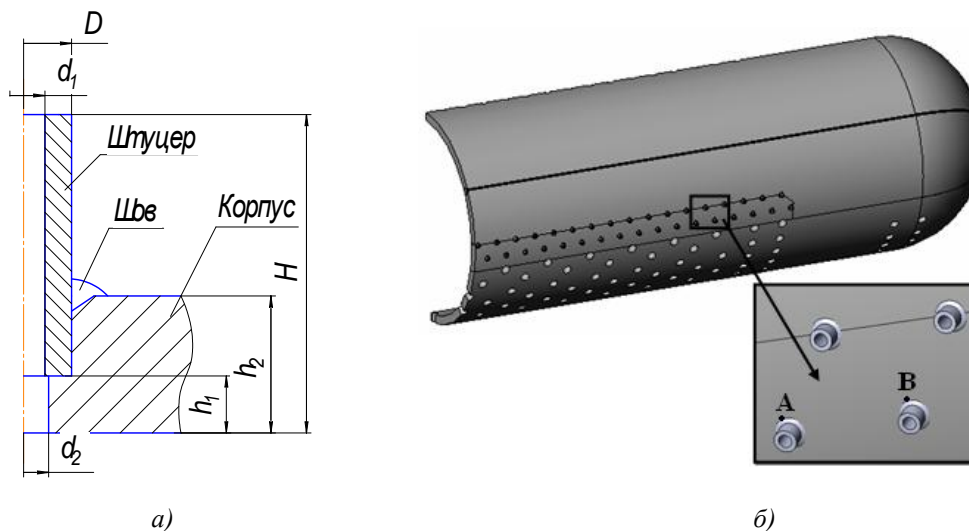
Схема штуцерного соединения(а) и твердотельная модель цилиндрического корпуса(б)
